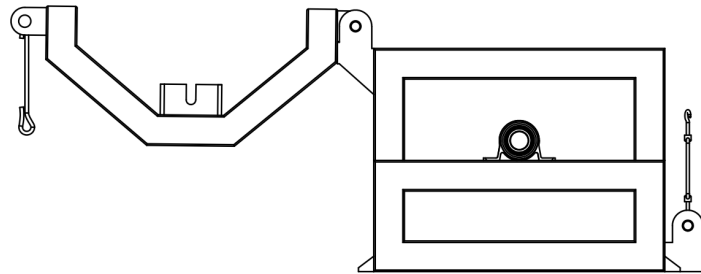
Vista lateral del ensamblaje de los soportes.
